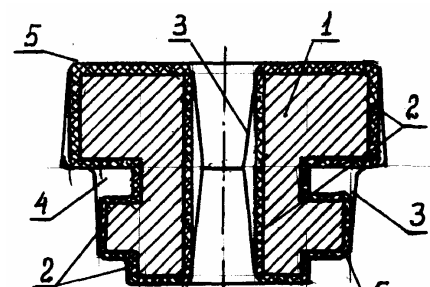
Чертеж штамповки, наложенный на чертёж детали
